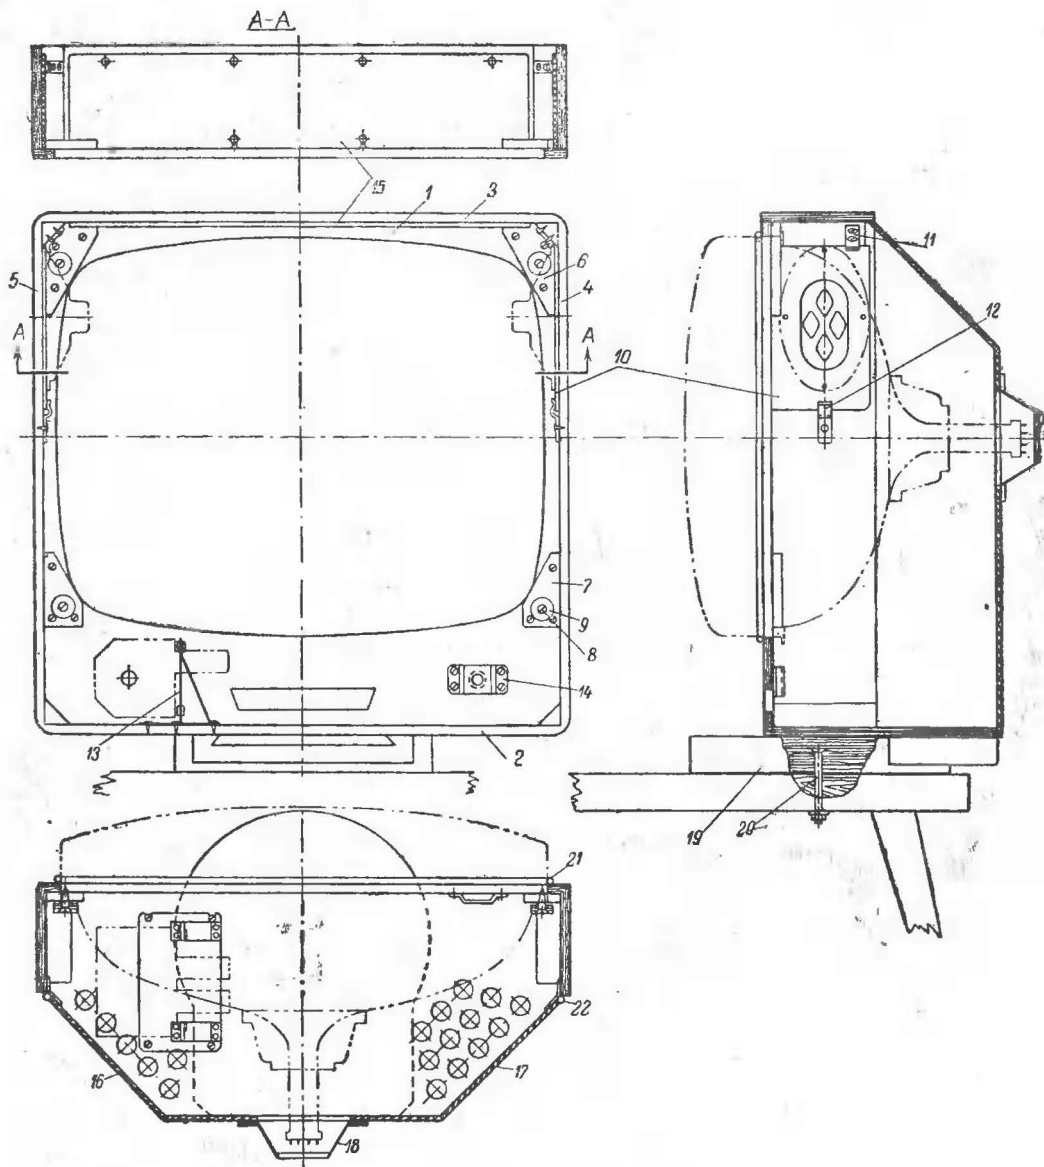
Общий вид ящика телевизора и поворотного устройства.
